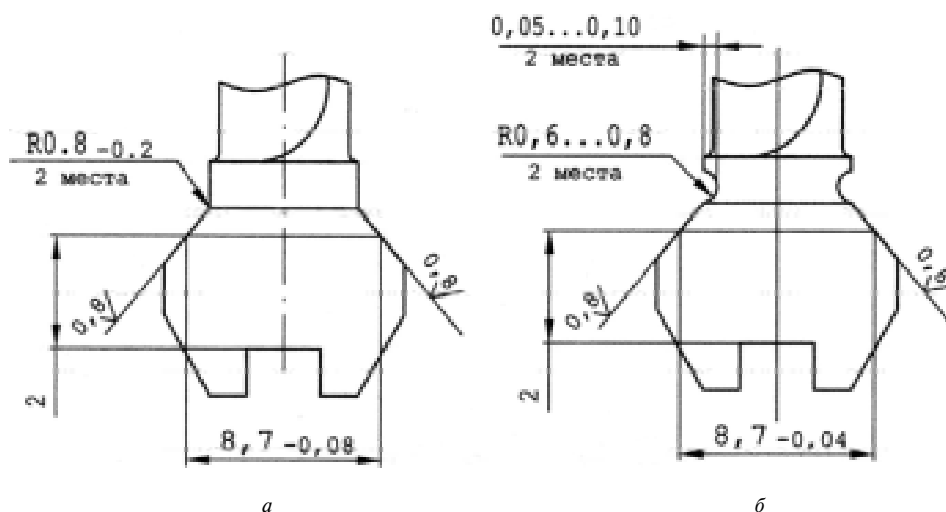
Вид замка лопатки II-й ступени КВД двигателя Д-36 (1 — со стороны спинки; 2 — со стороны корыта)
